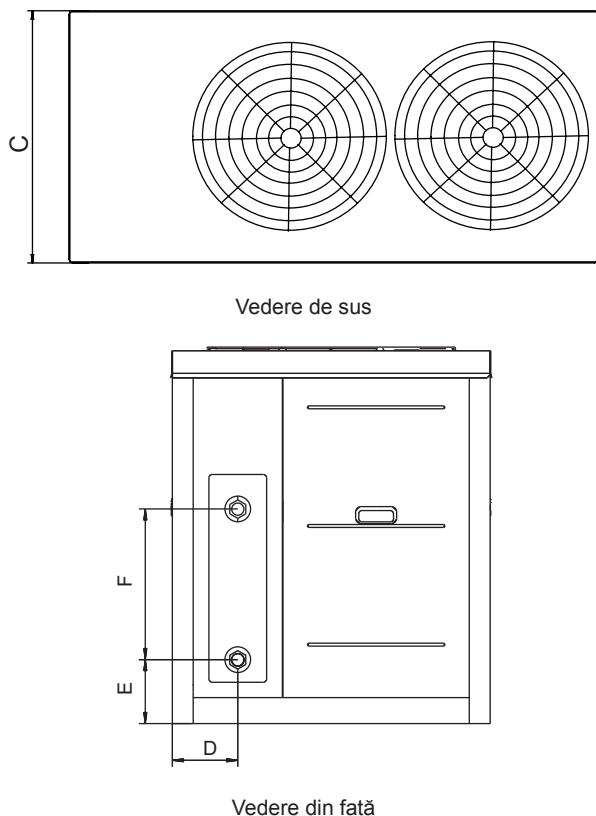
Schiță dimensională KEM-60 DNS3
